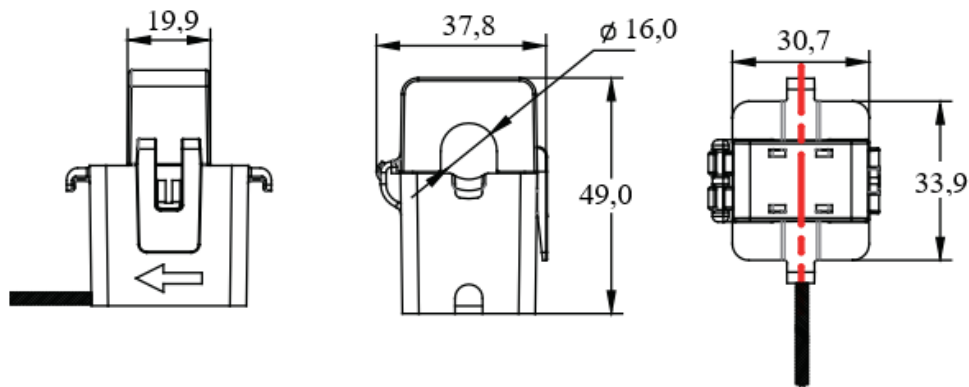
Внешний вид и габаритные размеры датчика SCT100
